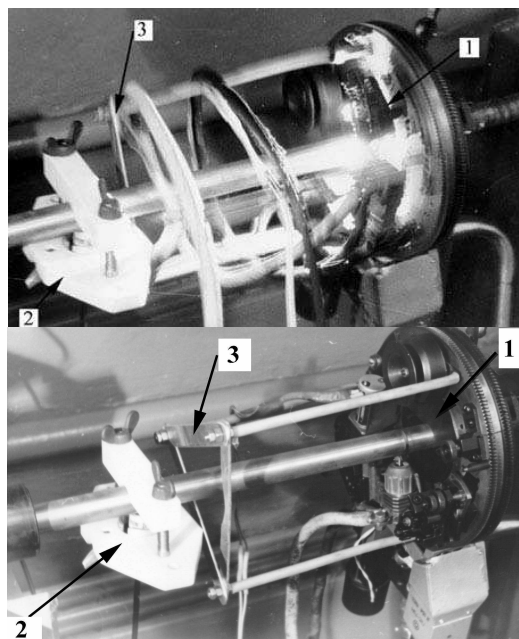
АЭ-контроль процесса сварки трубопроводов $\varnothing 20 \times 2$ мм из стали 08Х18Н10Т с помощью модернизированной головки типа ГНС-70М: 1) вкладыш из стали для крепления трубы; 2) блок крепления АЭ-пьезопреобразователя; 3) барабан для намотки кабеля, питающего сварочную головку. Внизу – после окончания сварки
